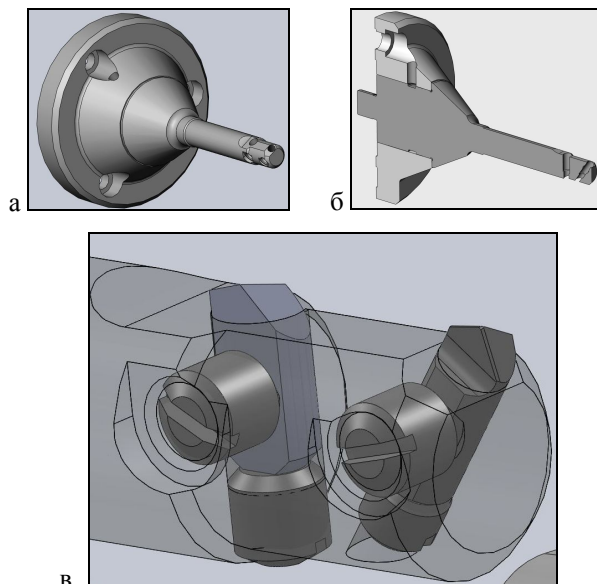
Борштанга с учетом недостатков аналогов: а – внешний вид; б – сборная конструкция; в – схема расположения резцов
